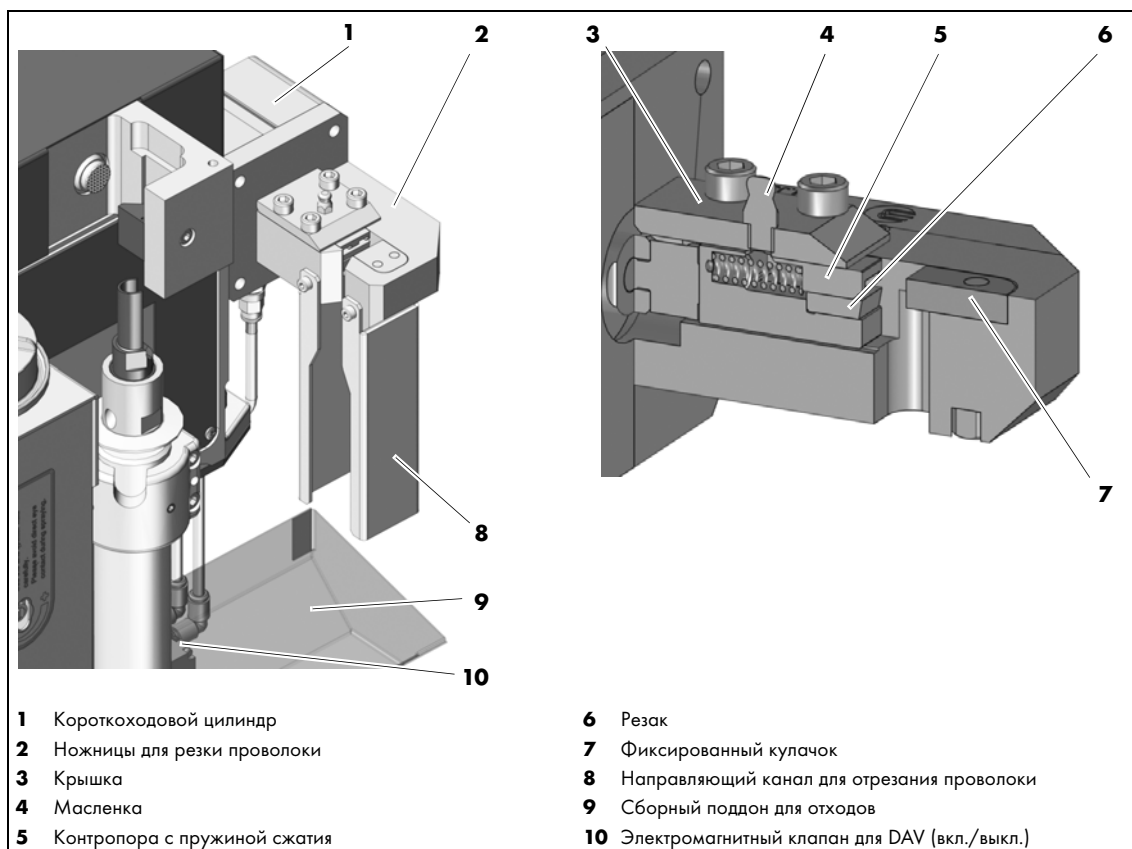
Устройство для откусывания сварочной проволоки
